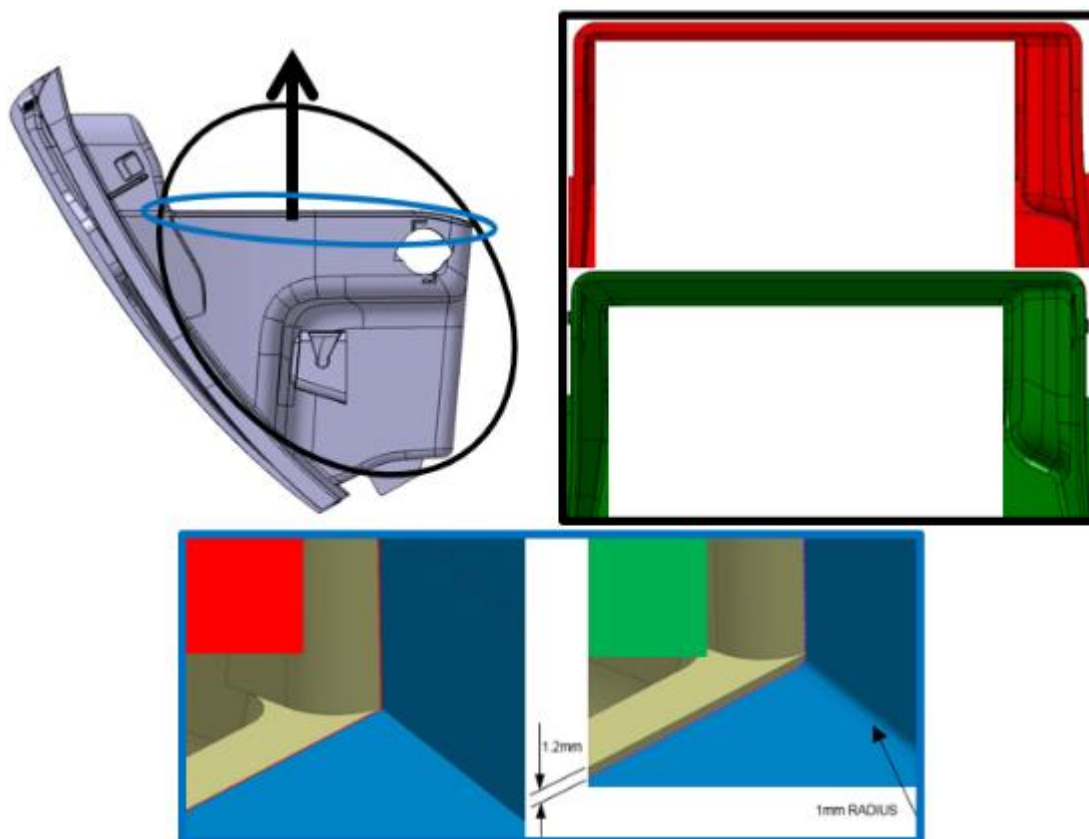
Designové změny dle směru šikmého vyhazování
